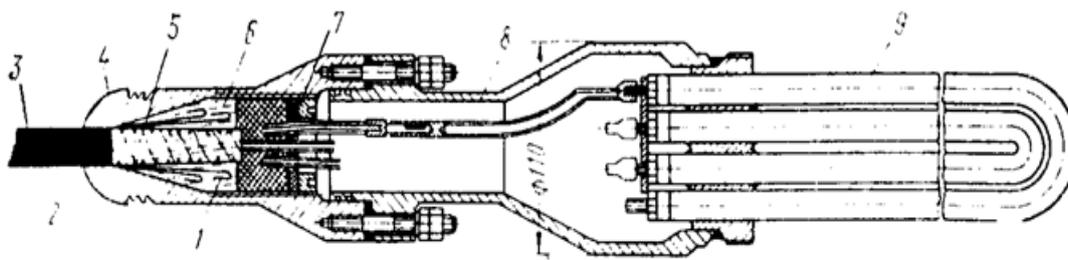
Глубинный электронагреватель: 1 – крепление кабель–троса; 2 – проволочный бандаж; 3 – кабель–трос КТГН–10; 4 – головка электронагревателя; 5 – асбестовый шнур; 6 – свинцовая заливка; 7 – нажимная гайка; 8 – клеммная полость; 9 – нагревательный элемент
